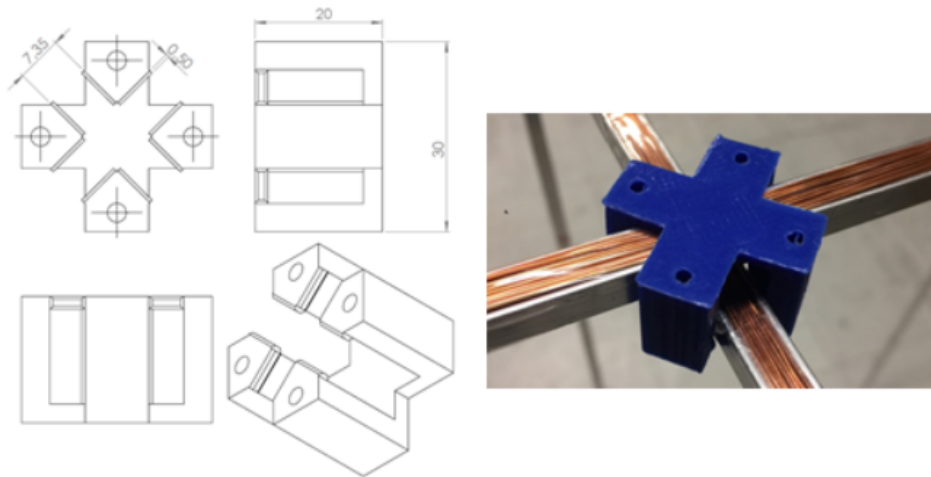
Soportes para el ensamblaje de las Bobinas de Helmholtz. [\[27\]](#)
